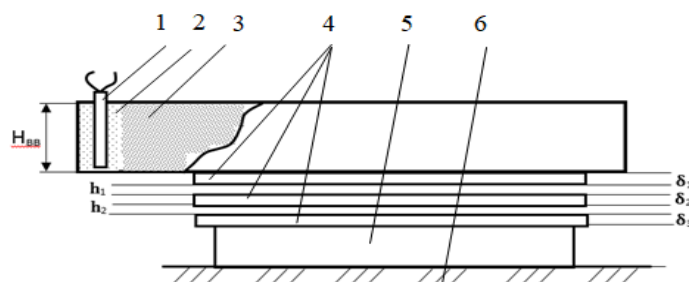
Схема сварки взрывом 3-слойного СММ с ВП:
